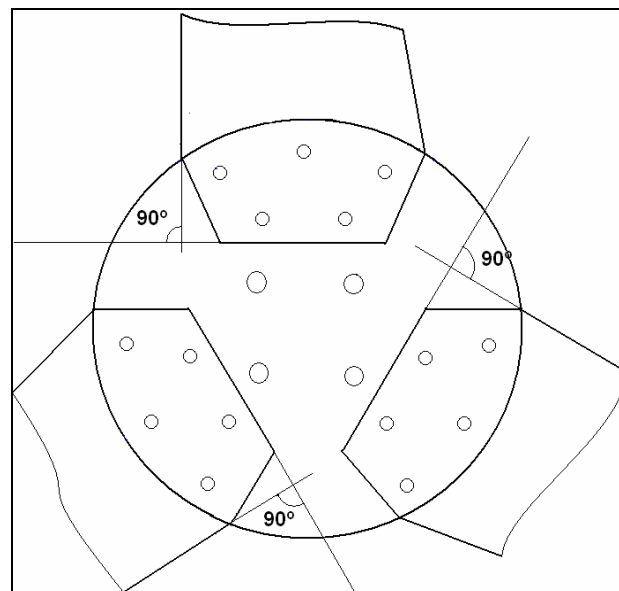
Posición de las palas sobre un disco del rotor eólico.
